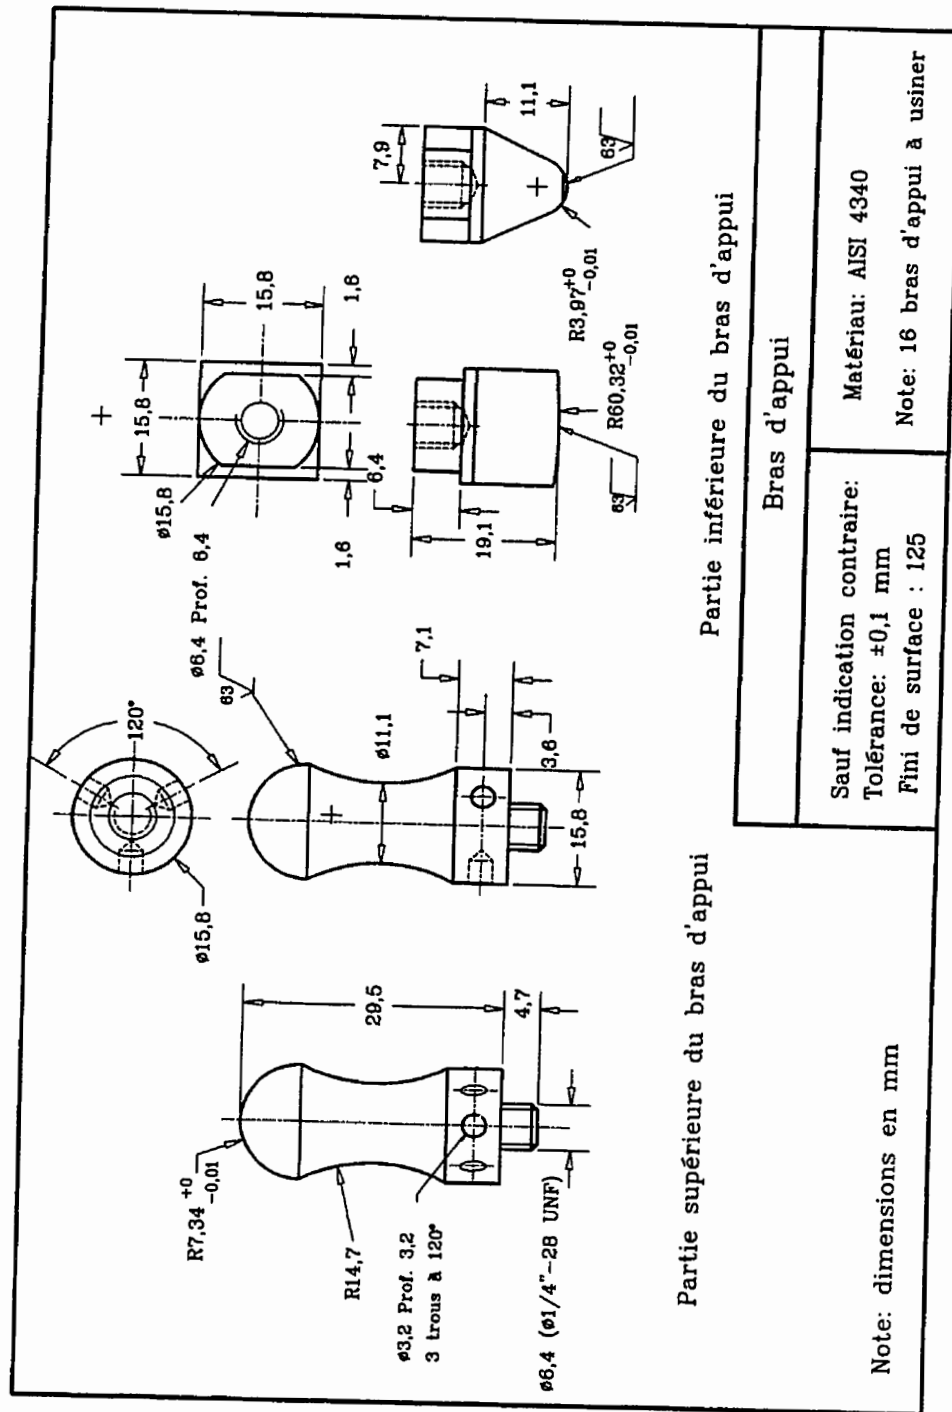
Géométrie et dimensions des bras de transfert de la charge
